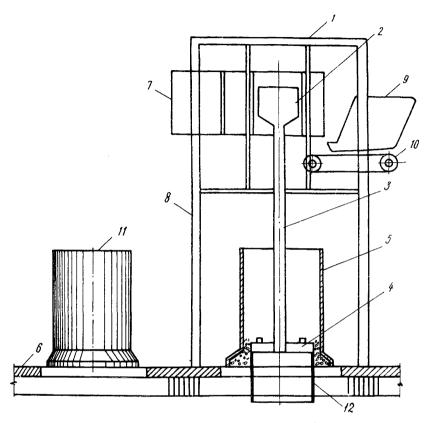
Схема станка для изготовления труб способом радиального прессования бетонной смеси I — станина; 2 — привод для вращения шпинделя; 3 шпиндель; 4 — прессующая головка; 5 — форма-опалубка трубы; 6 — поворотный стол; 7 — привод для подъема и опускания шпинделя; 8 — направляющие; 9 — бункер для приема бетонной смеси; IO — ленточный транспортер для загрузки формы; II — готовая труба; I2 — "фартук".
